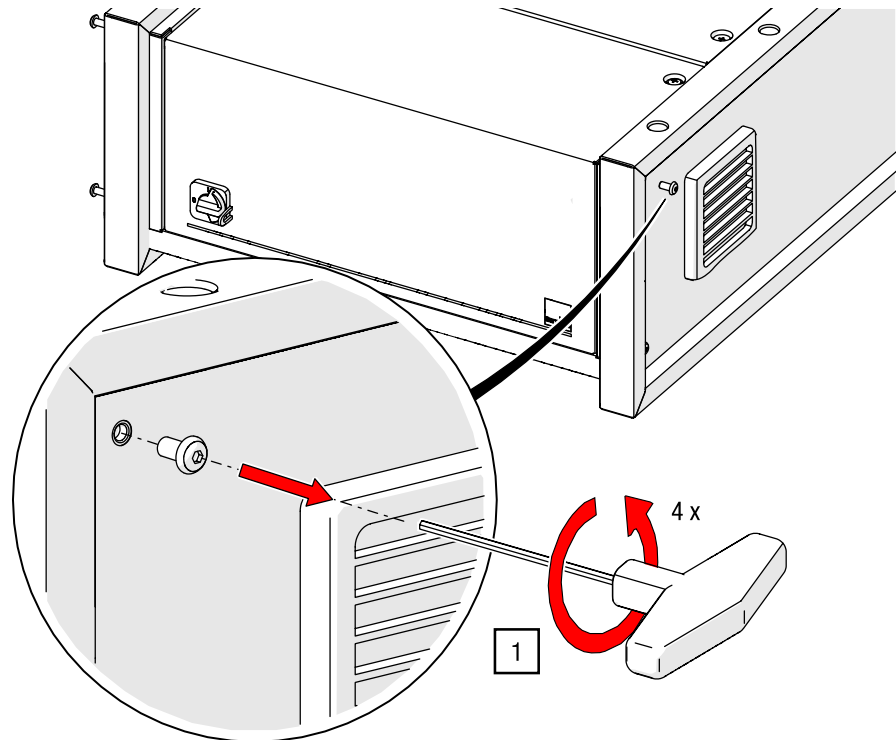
Steuerung G-FRAME Schrauben für die Montagewinkel lösen (Steuerungsmodell kann abweichen)
